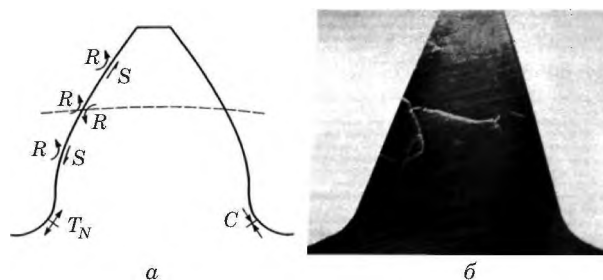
Области напряжений на основном зубе цилиндрического зубчатого колеса, развивающихся в зубе вследствие контакта качения R сопряженного зубчатого колеса — напряжений сдвига (S), растягивающих (T_N) и сжимающих (C) напряжений (а), а также пример растрескивания поверхностного слоя (б) с микротрещинами, перпендикулярными поверхности контакта [14]
